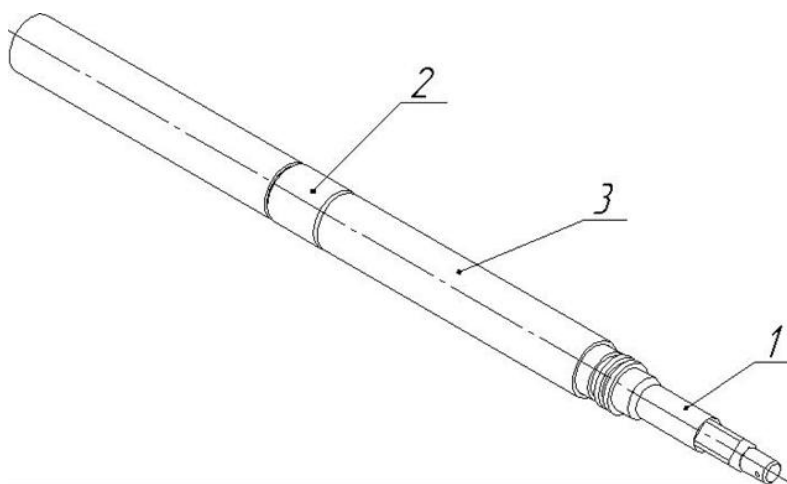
Ескіз приводного валу: 1 – вал, 2 – гайка, 3 – труба
